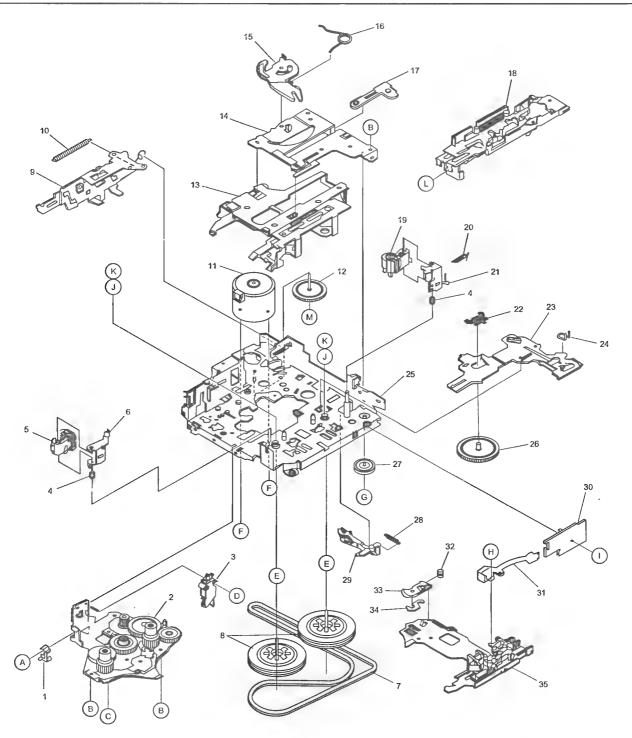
1 — замок храповика; 2 — основная приемная шестерня узла приемного и подающего подкассетника; 3 микропереключатель; 4 — возвратная пружина; 5 — прижимной ролик (левый); 6 — ограничитель механизма прижимного ролика; 7 — пассик; 8 — шкивы ведущего вала; 9 — неподвижная часть толкателя механизма выброса кассеты; 10 — возвратная пружина рычага толкателя выброса кассеты; 11 — электродвигатель; 12 — основная шестерня привода (левая); 13 — нижняя часть кассетоприемника; 14 — верхняя часть кассетоприемника; 15 — привод механизма выброса кассеты; 16 — возвратная пружина; 17 — ползун кассетоприемника; 18 — механизм ползунов перемотки и реверса в сборе; 19 — прижимной ролик (правый); 20 — блокирующая пружина механизма прижимного ролика; 21 — ограничитель блокирующей пружины; 22 — замок правой основной шестерни; 23 — подвижный механизм привода перевода направления движения главных шестеренок; 24 — фиксирующий замок; 25 — шасси ЛПМ; 26 — основная шестерня привода (правая); 27 — средний шкив; 28 — возвратная пружина; 29 — толкатель; 30 — планка крепления механизма магнитной головки; 31 — шлейф магнитной головки; 32 — ролик; 33 — подвижный замок механизма магнитной головки; 34 — фиксирующий замок механизма магнитной головки; 35 — механизм магнитной головки; А— винт самонарезной; В— винт M2; С— винт самонарезной; D— винт крепления M2,5; Е шайба (фторопласт); F — винт крепления M2,5; G — установка на ось; Н — винт крепления M2,5; J, К шайба; L — винт крепления М2,5; М — шайба
